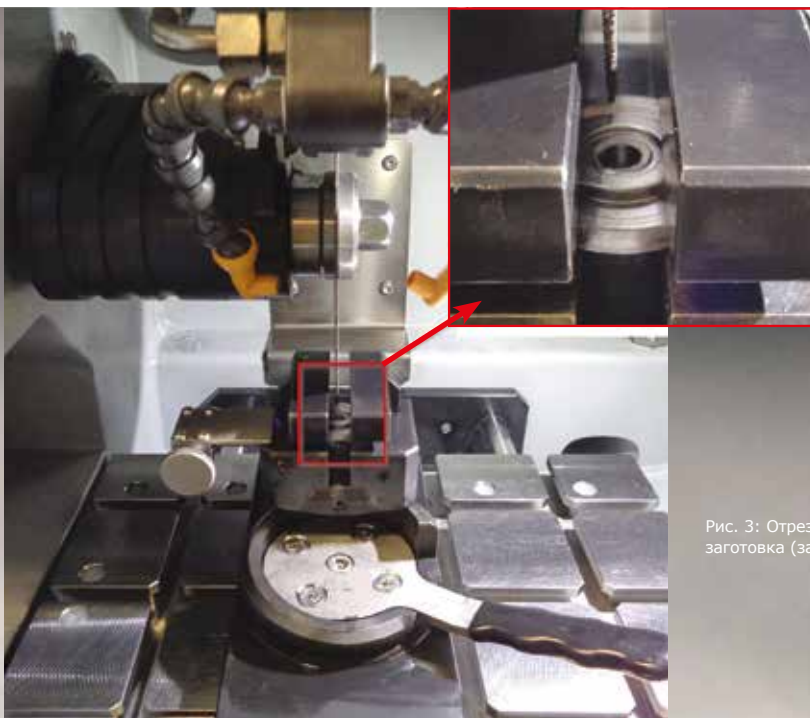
Отрезной станок Brilliant 220. В увеличенном масштабе: закрепленная заготовка (зажимной инструмент: одинарные вертикальные тиски).
